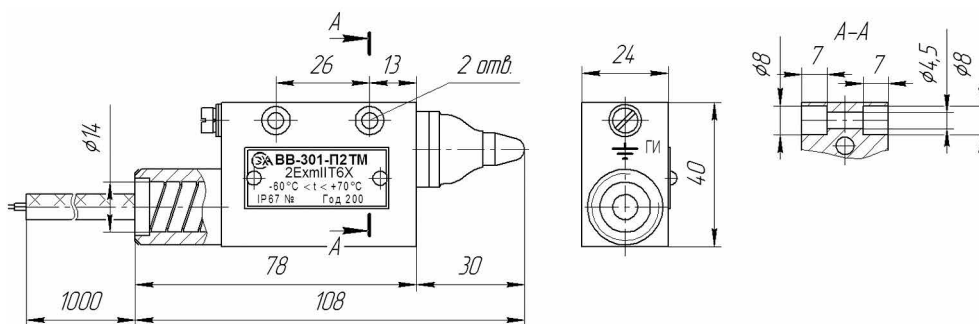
Габаритные и установочные размеры ВВ-301-П2ТМ
